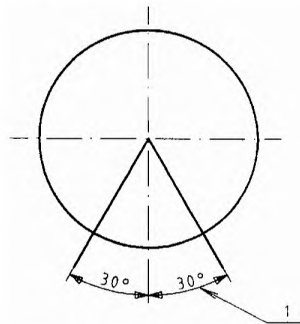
Швы сварных соединений с полным проплавлением для труб, штуцеров и муфт
